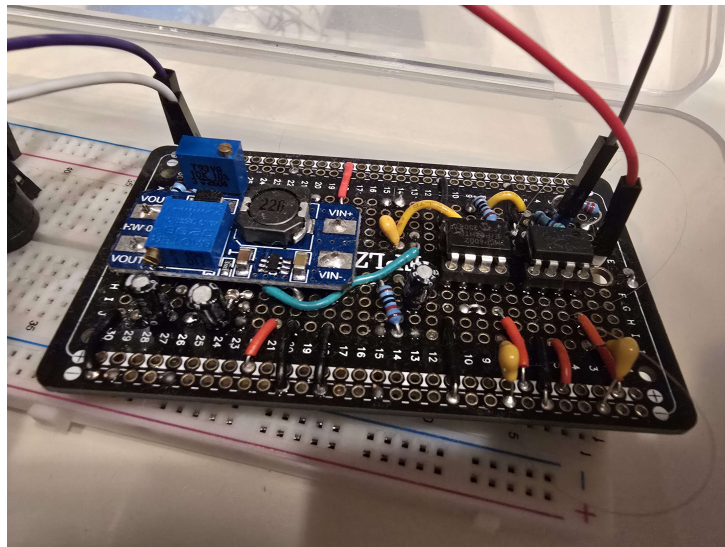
Carte de prototypage soudée (Perfboard)
